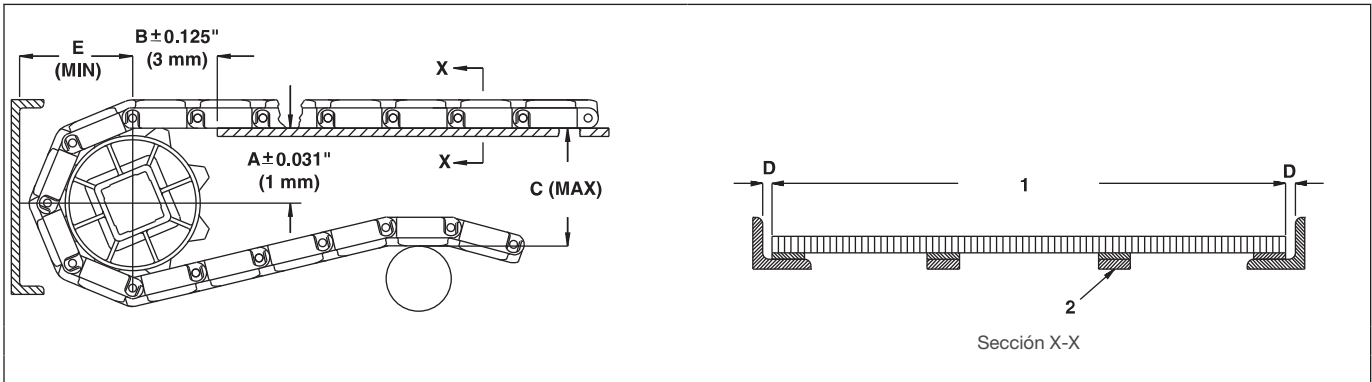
Requisitos de dimensiones básicas (retorno del rodillo)
